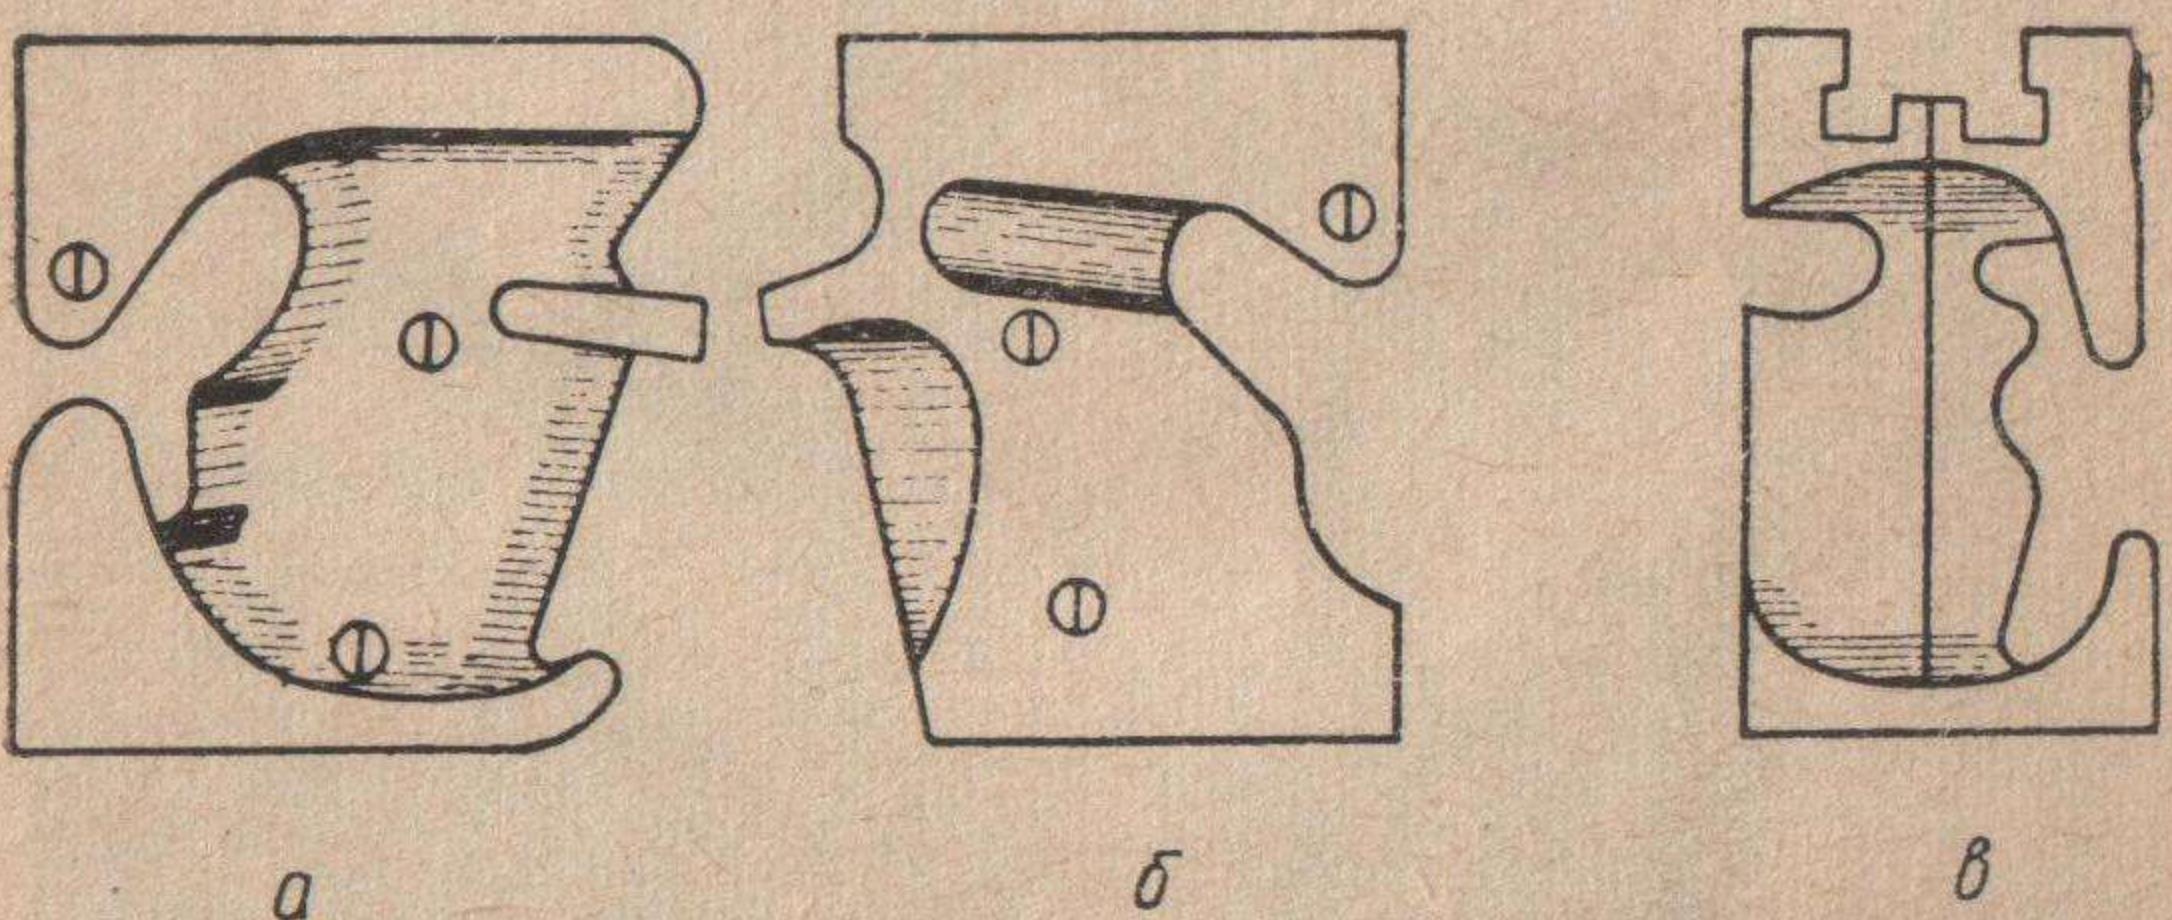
Форма рукоятки, изготовленная из дерева: а — правая сторона; б — левая сторона; в — в сборе (вид сзади)
